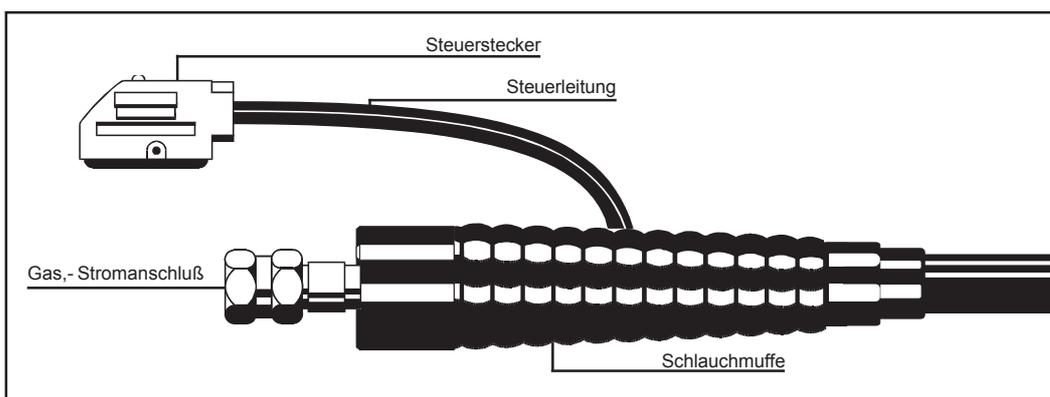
Ausführung mit Brenner-Zentralanschluß GWZ: Brenneranschluß gasgekühlt
